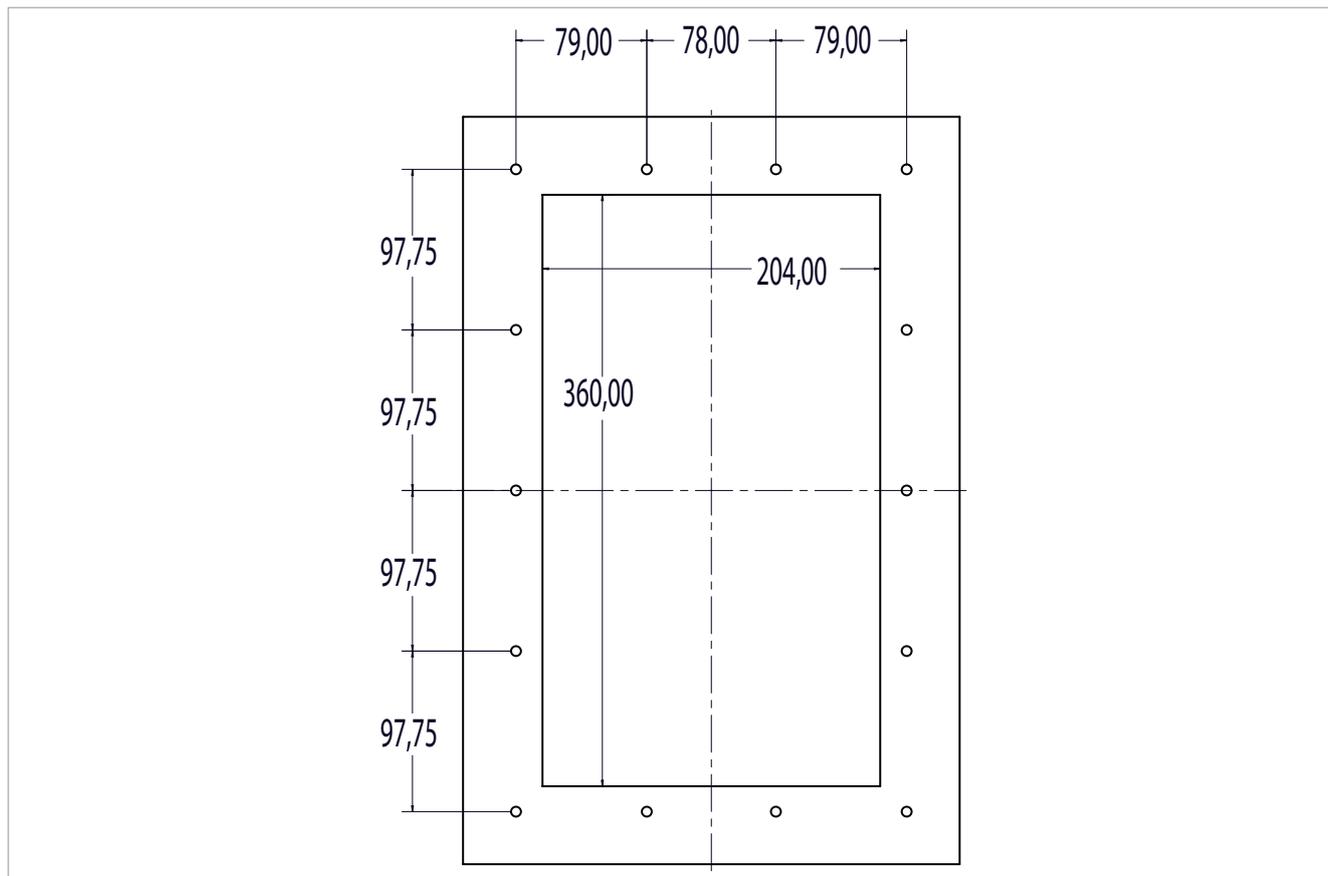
Maße Ausbruch für Durchsteckkühlkörper [mm]
